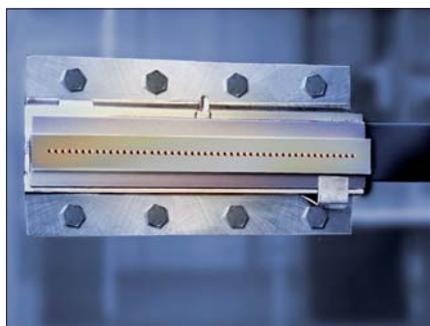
Detalhe do elemento de aquecimento a gás, instalado na soldadora apresentada pela Bielomatik
